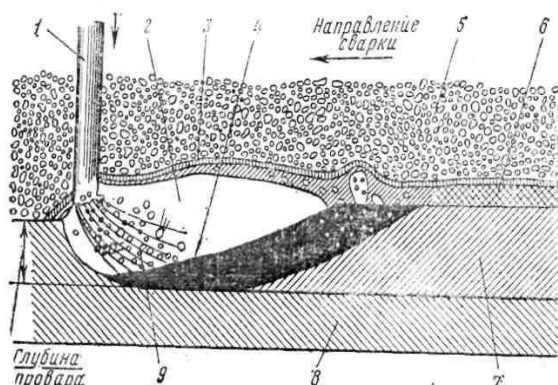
Схема горения сварочной дуги под флюсом
